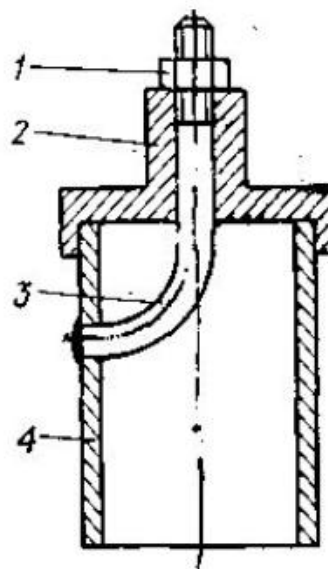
Приварка шпильки до корпусу ковпачка
